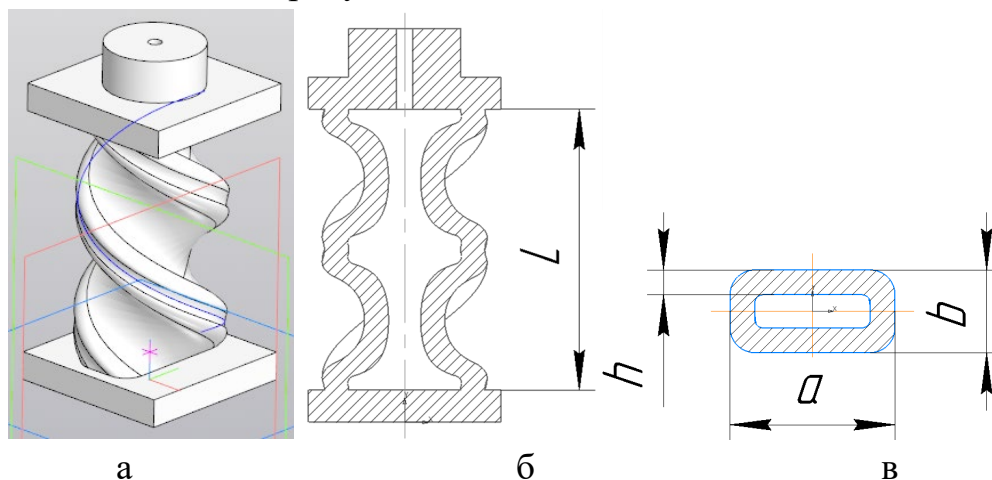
Двухкамерный поворотный актуатор спиралевидной формы
